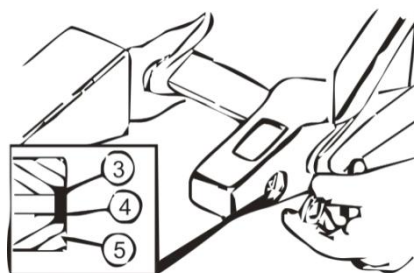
9. Расположение кольца, шайбы и втулки на адаптере
